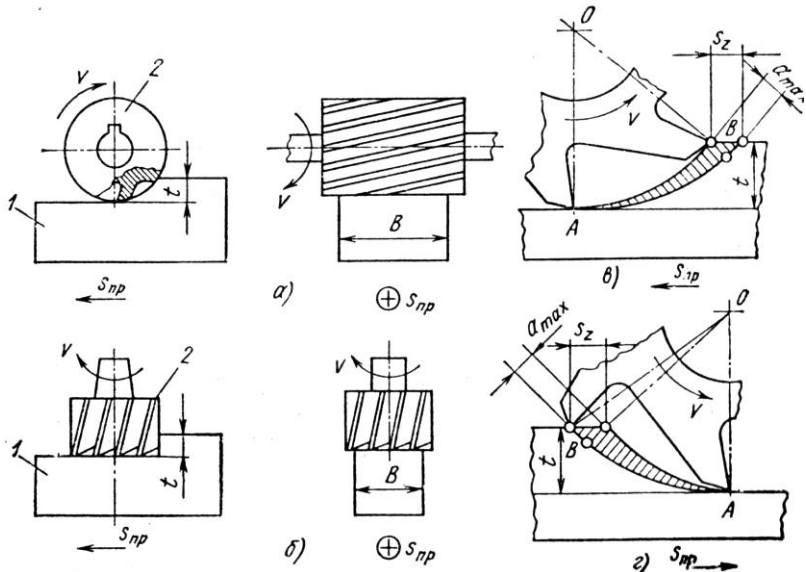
Схемы фрезерования цилиндрической (а) и торцовой (б) фрезами, встречного (в) и попутного (г) фрезерования:
